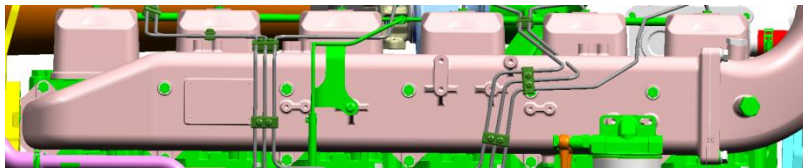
Assemblage et installation de la pipe d'admission d'air (le dispositif de préchauffage n'est pas monté)
